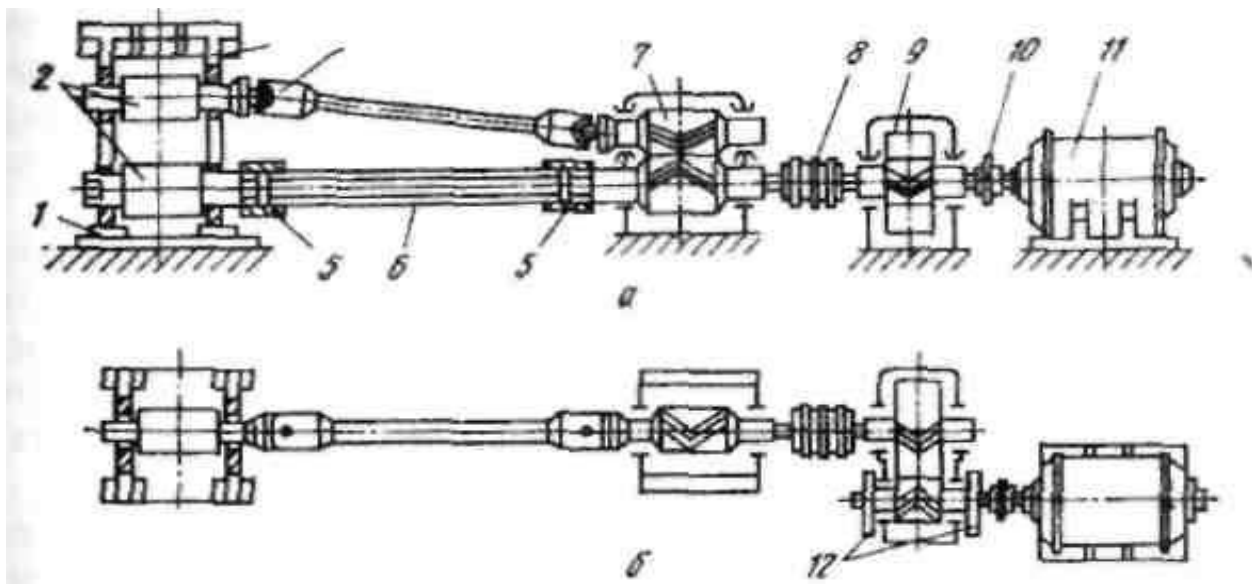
Схема одноклетьевого стана: а-вид спереди; б-вид с верху; 1-плитовина; 2-валки; 3-рабочая клеть; 4-шпиндель; 5-соединительные муфты; 6-трефовый шпиндель; 7-шестерённая клеть; 8-коренная муфта; 9-редуктор; 10-моторная муфта; 11-главный электродвигатель; 12-маховики
